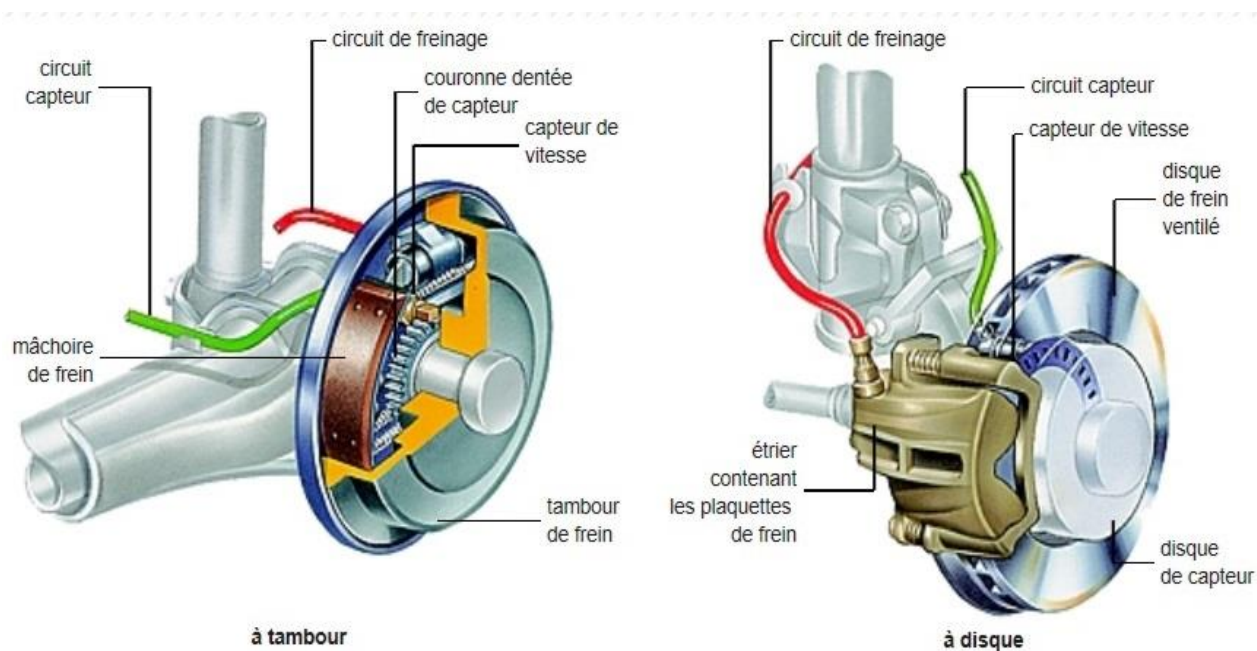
Freins d'automobile à tambour et à disque [6]
